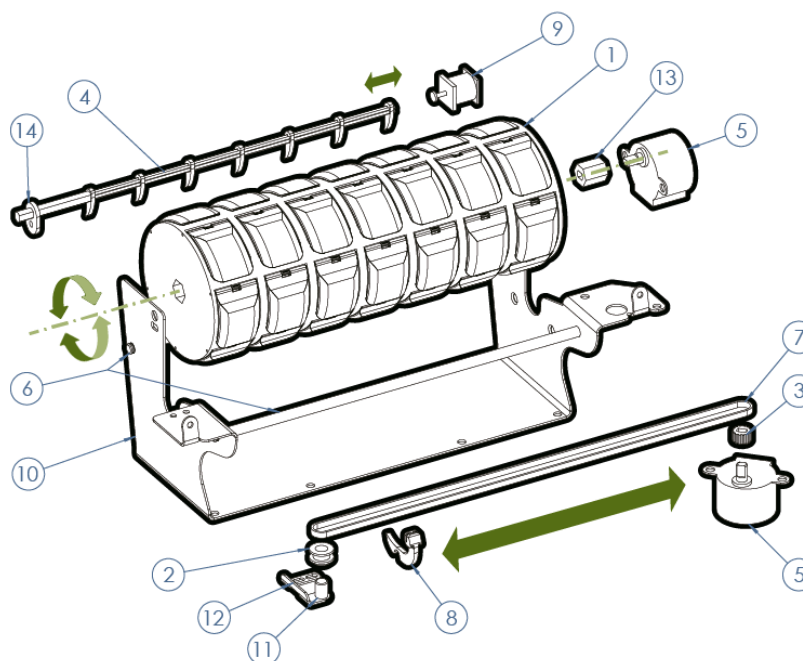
Vista explodida do sistema dispensador de medicamentos.
